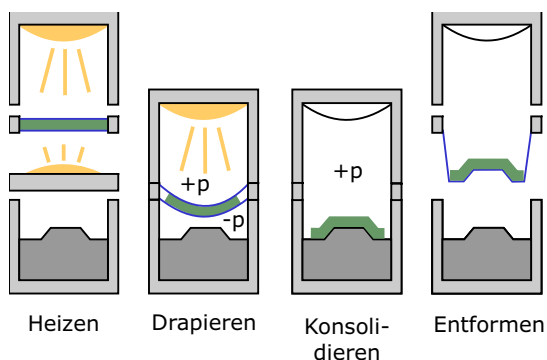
rfZ) Prinzip der Diaphragmatechnik
